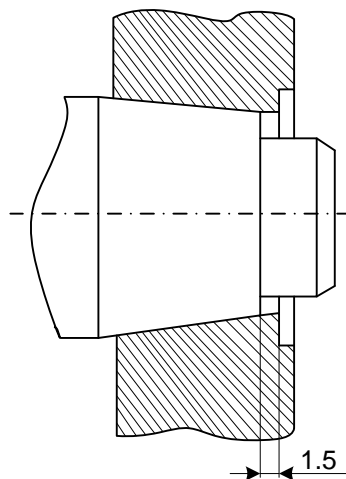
Посадка шестерни на вал якоря ТЭД
